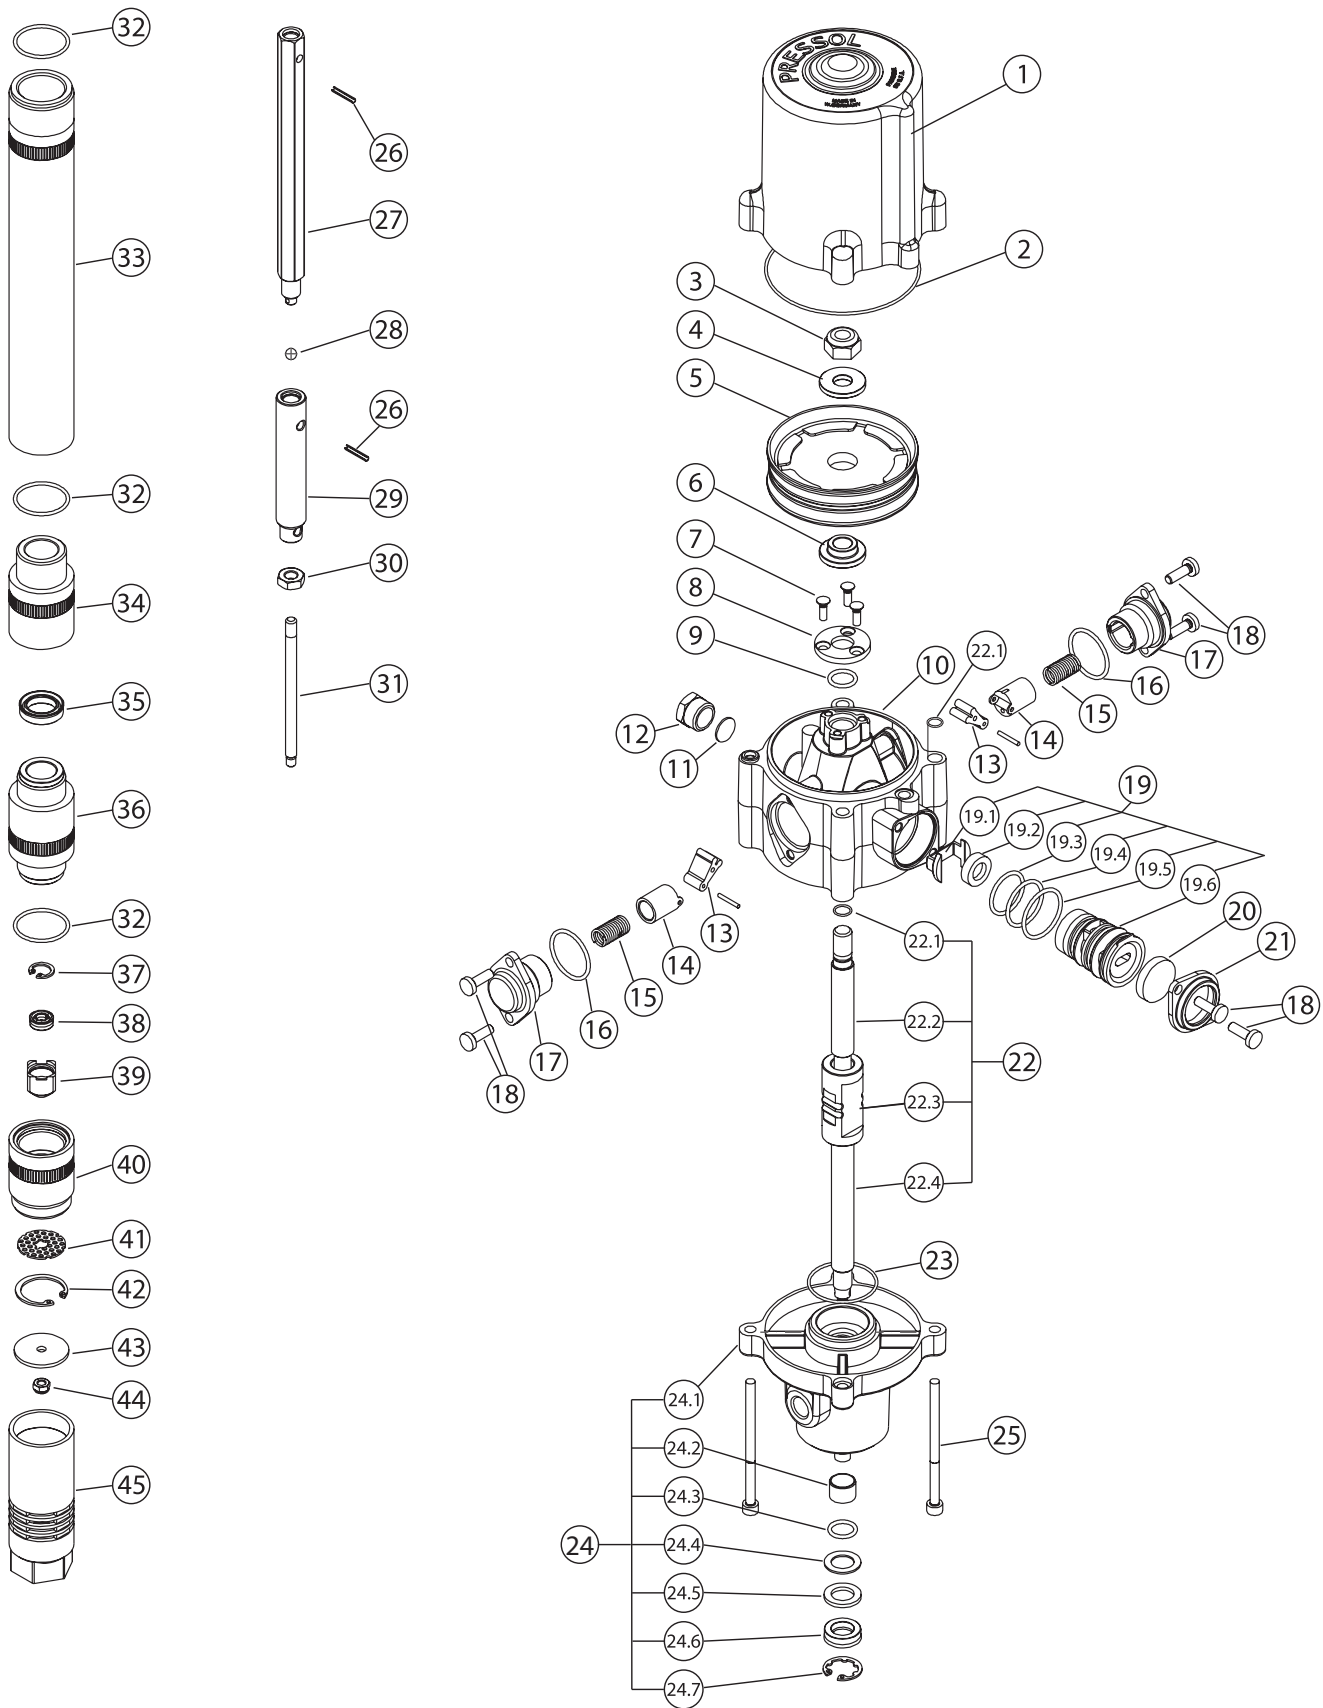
Vue éclatée de la pompe pneumatique graisse
